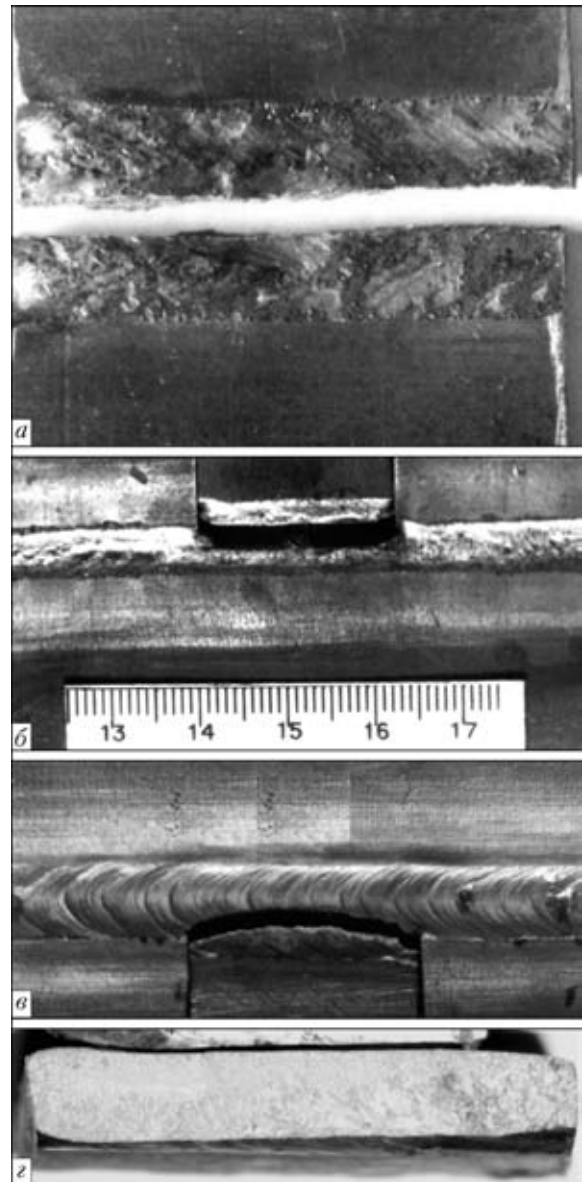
Внешний вид и расположение изломов замедленного разрушения образцов соединений, сваренных за два прохода без (а, б) и с усилением шва (в) без (а) и с искусственными концентраторами напряжений (б, в); г — поверхность излома
